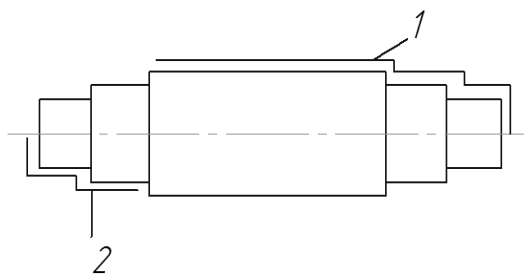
Поверхні 1 і 2 вала, які оброблюються при різних установах
